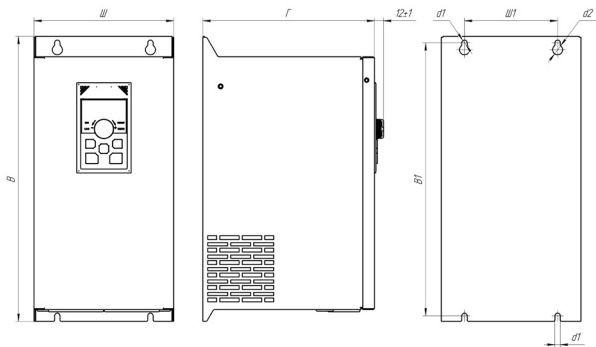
Установочные и габаритные размеры тормозного модуля BU, типоразмер 3
